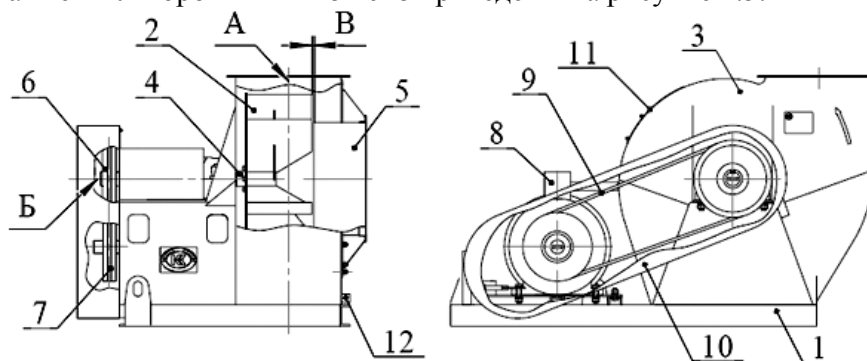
Вентиляторы ВРП-115-49-8. Конструкция и состав.
